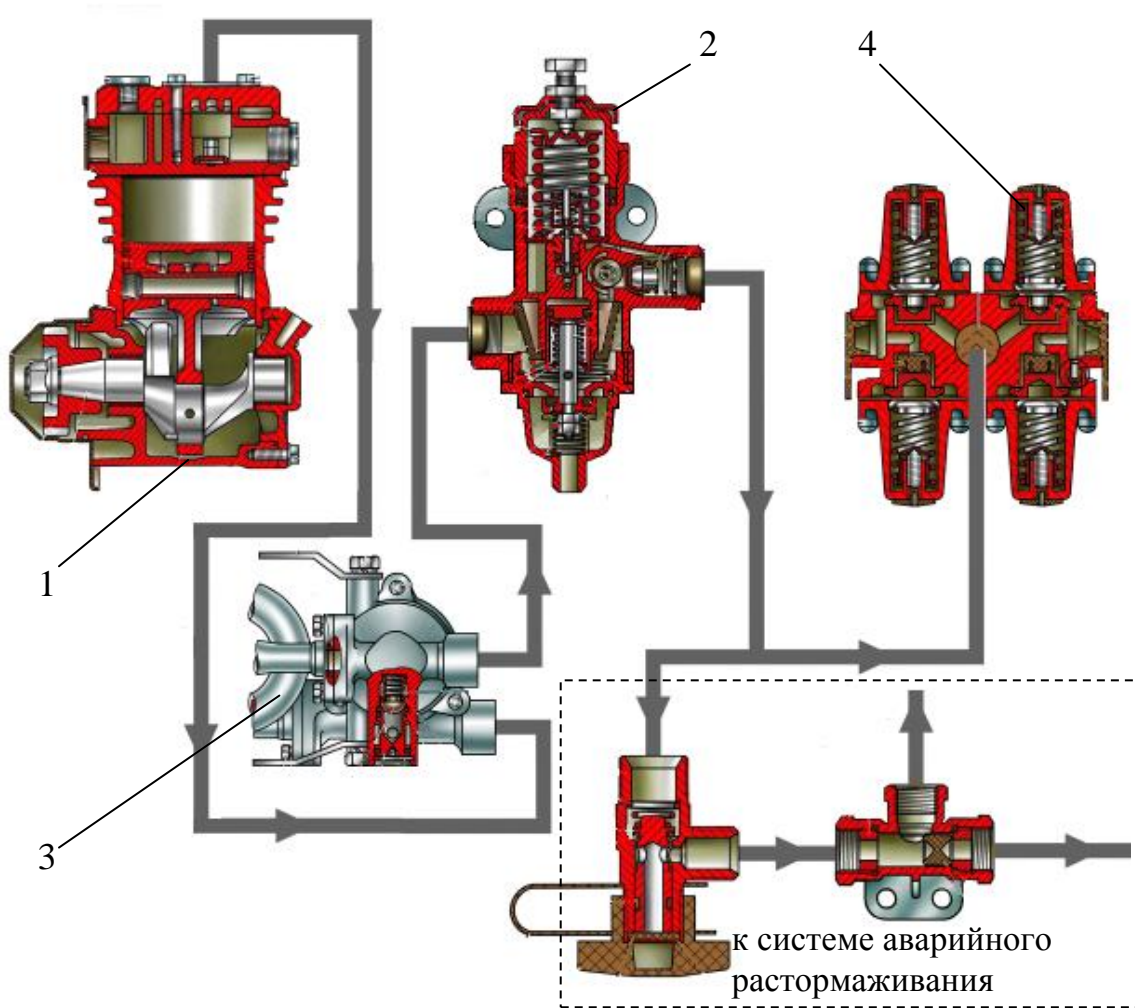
Схема участка питания пневматической системы тормозного привода грузового автомобиля-тягача КАМАЗ-5350: 1 – компрессор; 2 – регулятор давления; 3 – водоотделитель; 4 – четырехконтурный защитный клапан
